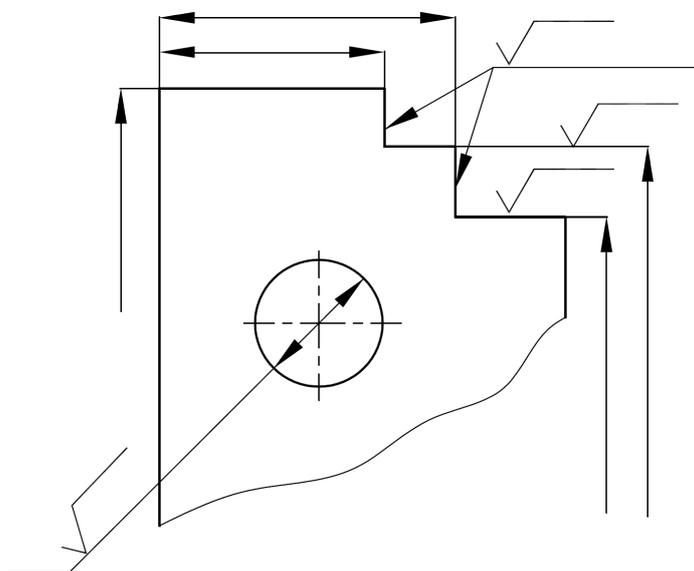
Нанесение обозначений шероховатости поверхностей на изображении изделия
